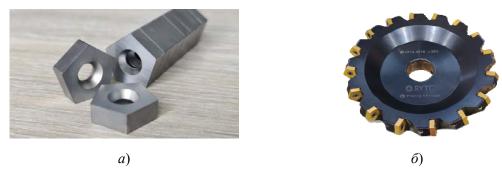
Вид спеченной твердосплавной пластины PNUQ 13T709 (*a*), фреза BYTC/OИЗ для силового фрезерования (δ)
